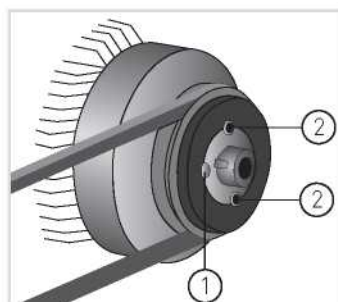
центровка шкивов и натяжение клинового ремня
